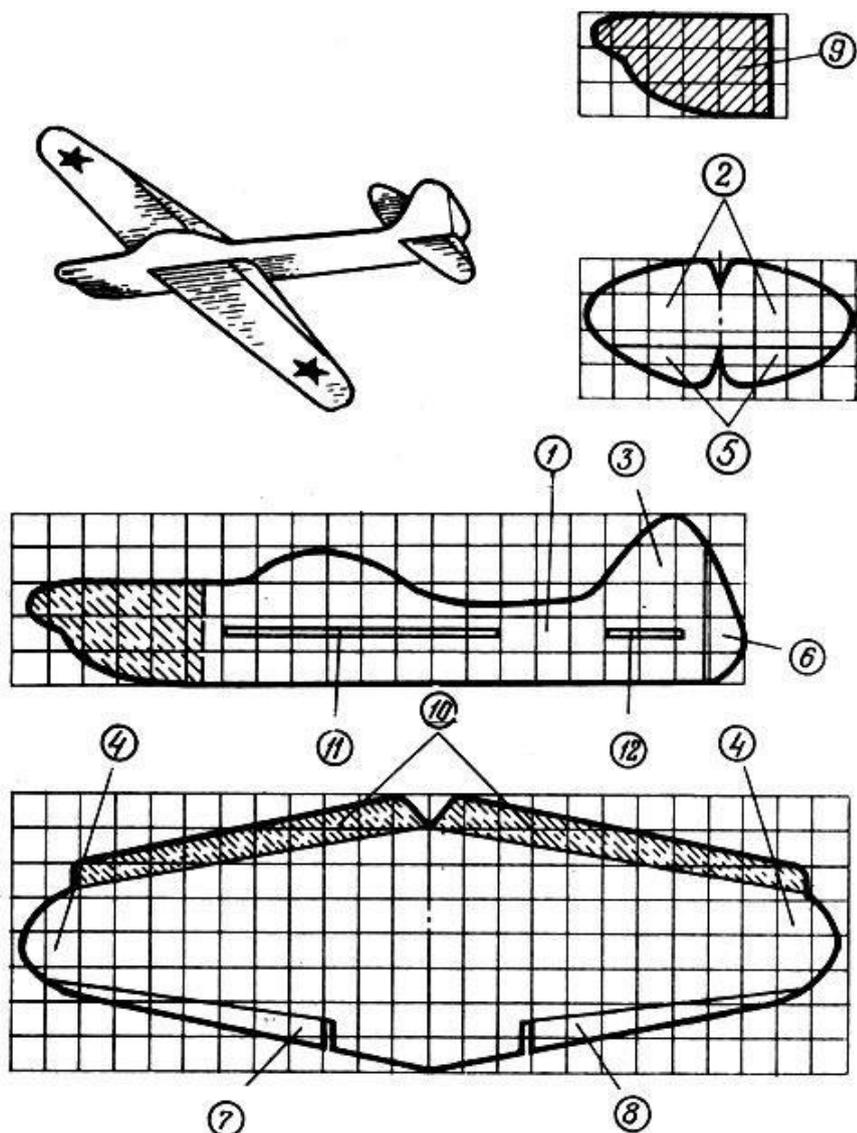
Модель самолета Як-3: 1 - фюзеляж; 2 - стабилизаторы; 3 - киль; 4 - крылья; 5 - руль высоты; 6 - руль поворота; 7 - левый элерон; 8 - правый элерон; 9 - груз из картона; 10 - клапаны, образующие переднюю кромку крыла (при подклеивании); 11 - прорезь для крыльев; 12 - прорезь для стабилизатора
